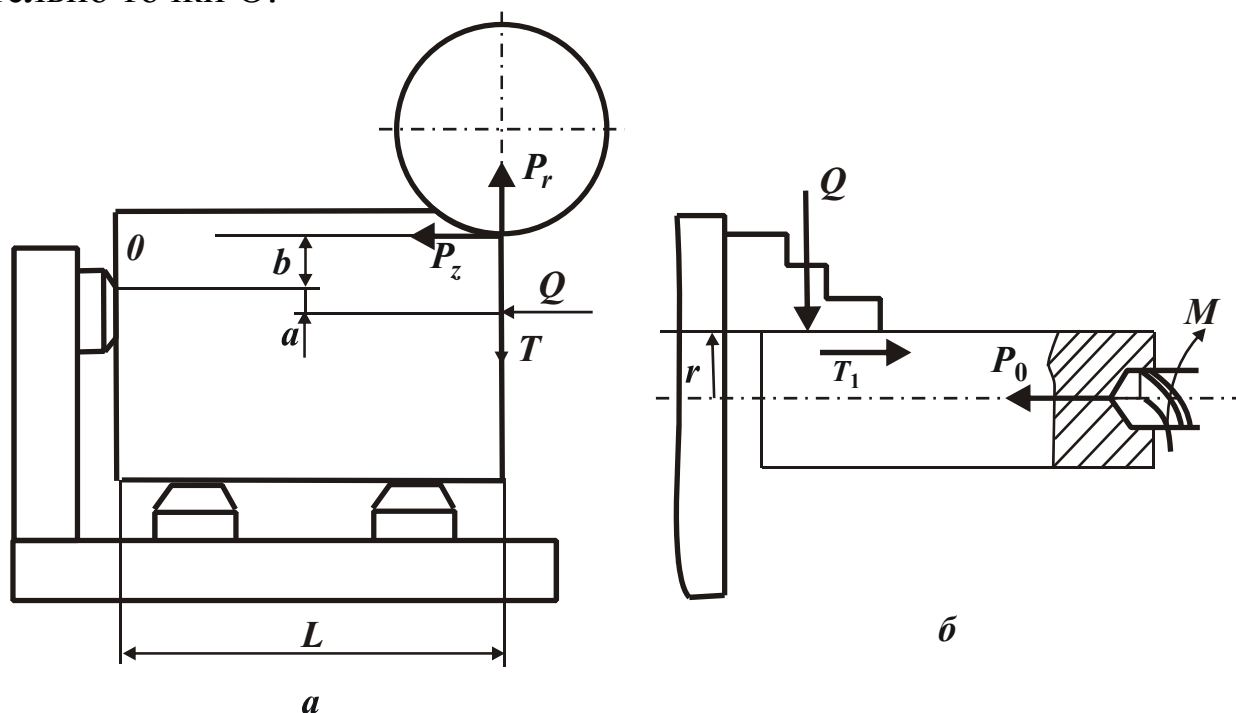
Схемы к определению величины зажимного усилия, удерживающего заготовку: а - при фрезеровании; б - при сверлении на токарном станке.
